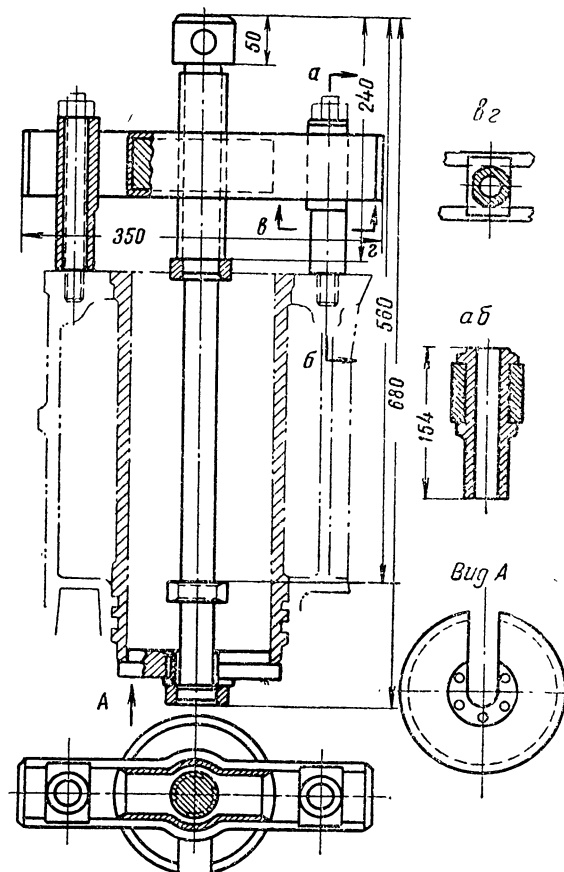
Приспособление для выпрессовки и запрессовки гильзы.
